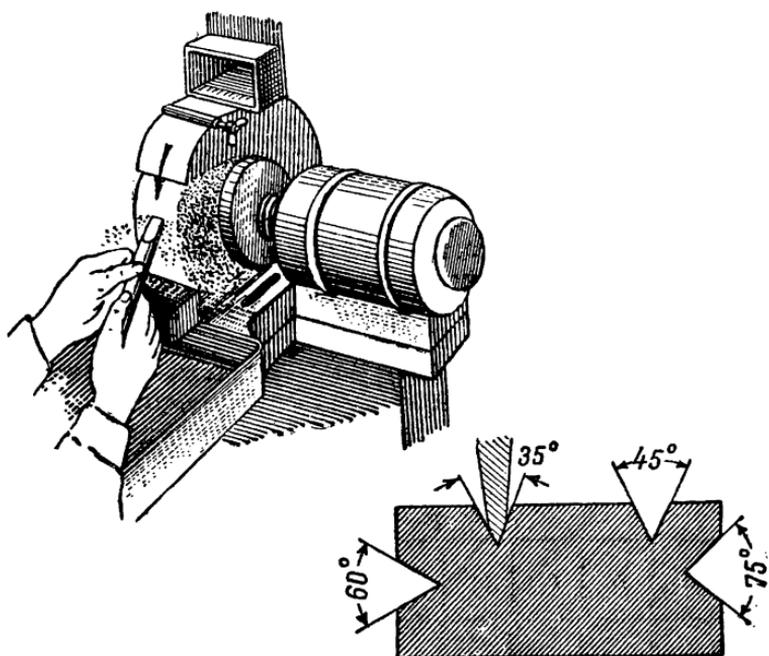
Заточка зубила и шаблон для проверки угла заострения.
